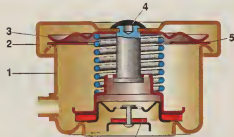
Передельная пробка радиатора "Волги" ГАЗ-21: 1 - горловина радиатора; 2 - корпус пробки; 3 - дисковая пружина; 4 - место пайки; 5 - резиновая прокладка (новая деталь); 6 - впускной клапан (пружина удалена).
